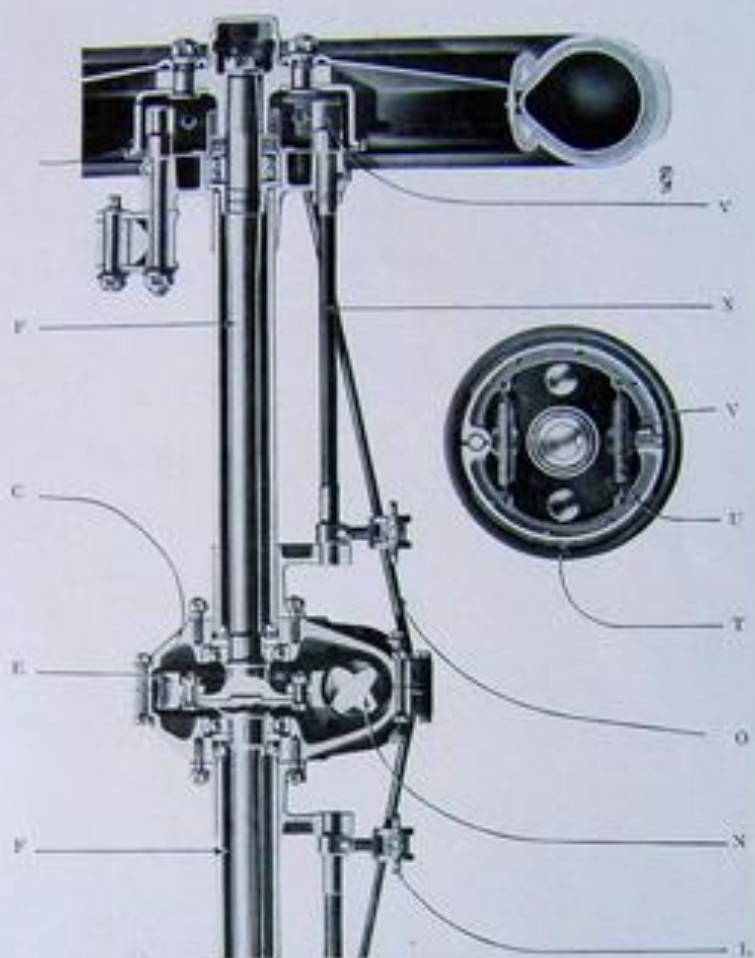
COUPE DU PONT ARRIÈRE ET VUE D'UN FREIN.
